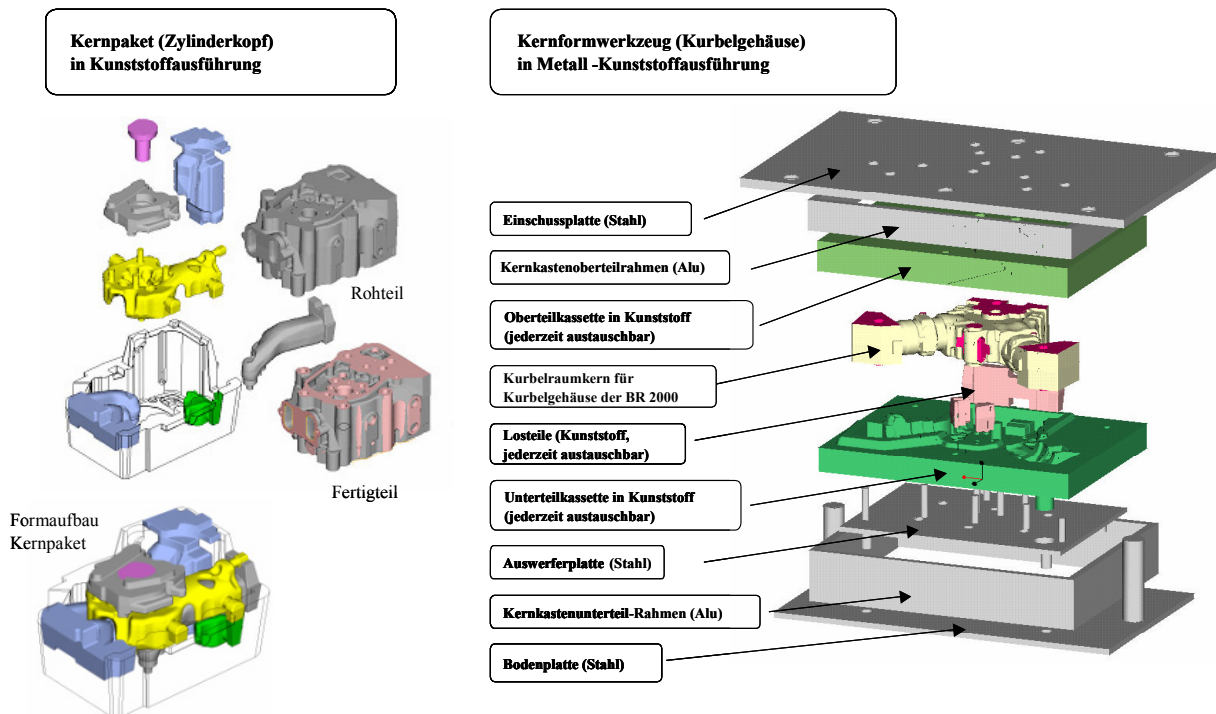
3D-CAD-modelliertes Kernpaket und Kernformwerkzeug
